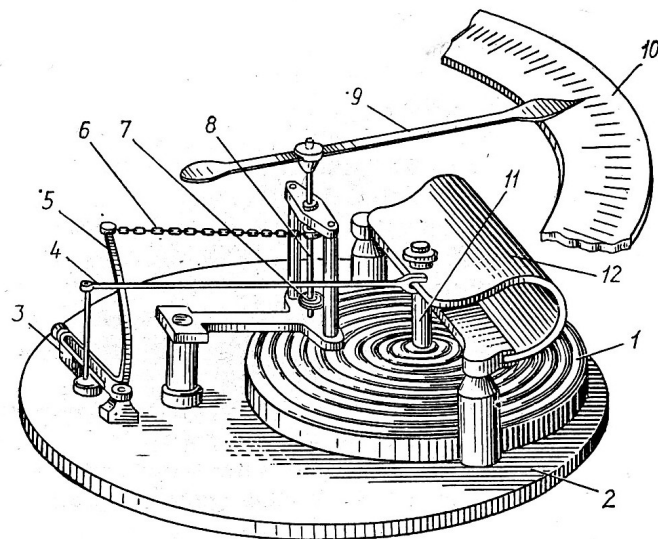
Механізм барометра-анероїда БАММ-1: 1 – анероїдна коробка; 2 – металеве плато; колінчастий вал; 4 – стрижень; 5 – важіль; 6 – ланцюг; 7 – пружина; 8 – вісь; 9 – стрілка; 10 – шкала; 11 – ніжки; 12 – пружина
